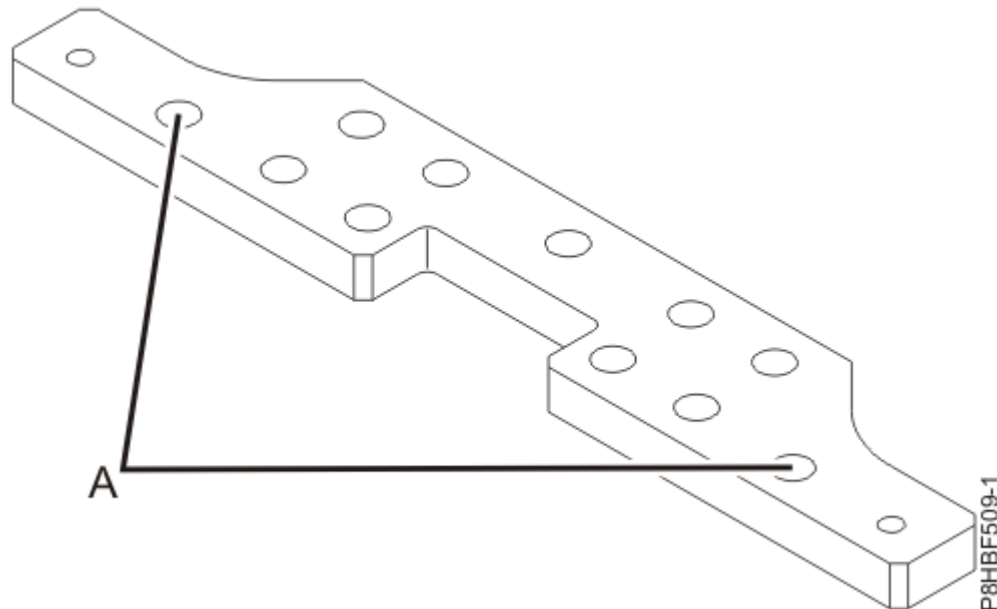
Localizações de furos da placa do parafuso inferior para rack com a chave triangular
